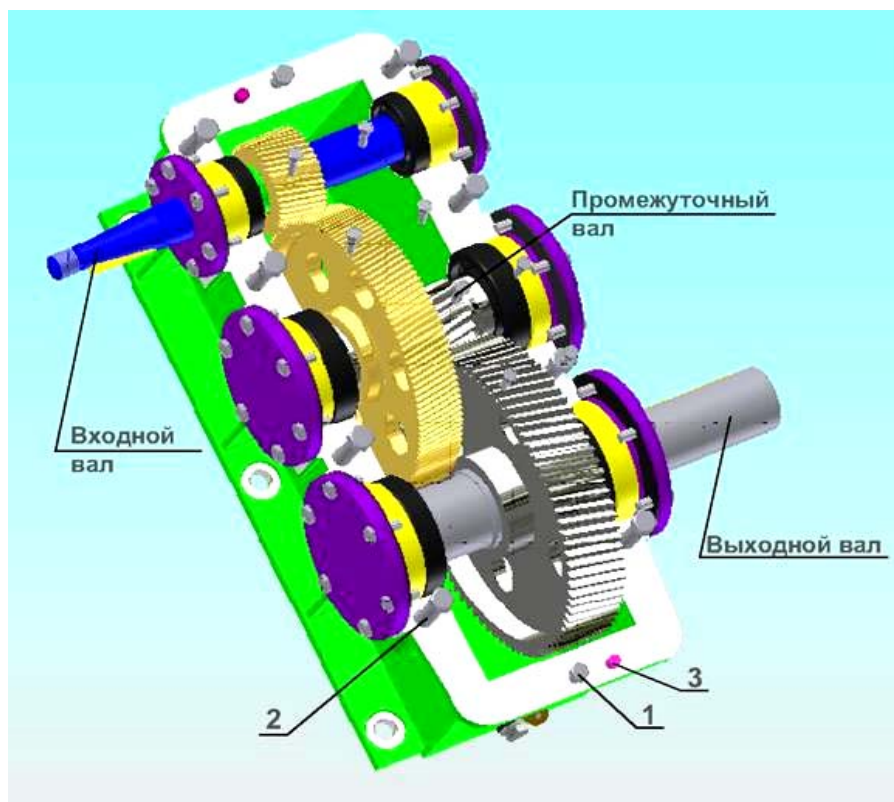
Внешний вид редуктора без крышки: 1 – болты крепления крышки и корпуса редуктора; 2 – болты для соединения корпуса и крышки редуктора, установленные в бобышки (приливы у подшипниковых узлов); 3 – штифты для фиксации крышки
